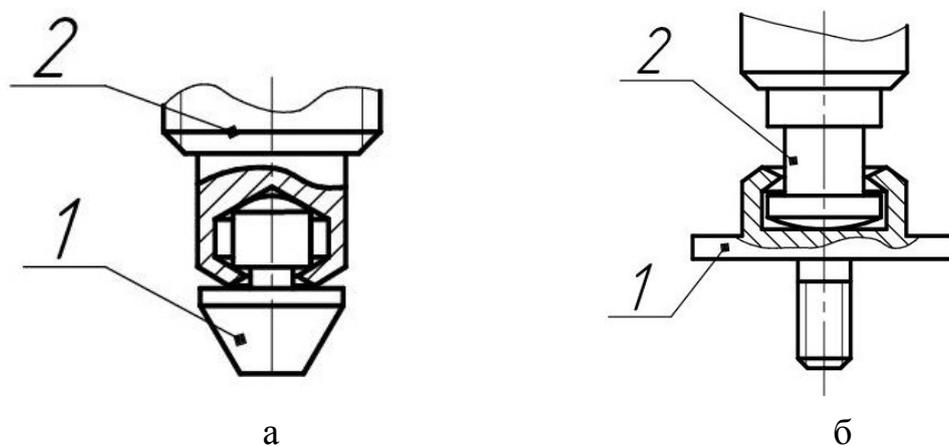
Неразъемные подвижные соединения шпинделя с клапаном:
